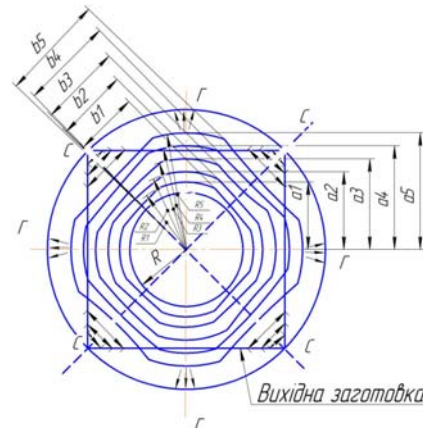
Схема течії металу в фланцевій частині деталі при штампуванні обкочуванням з кільцевої заготовки. Г - Г - лінія переобладнення радіальної течії металу С - С - лінія переобладнення тангенціального течії металу
